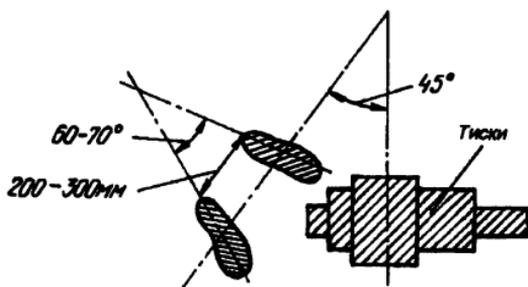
Положение ног и корпуса при рубке металла
